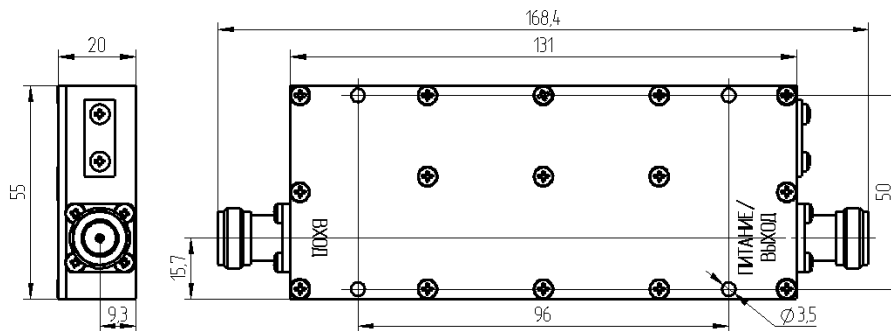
Внешний вид и габаритные размеры МШУ 2483,5-2500 МГц
